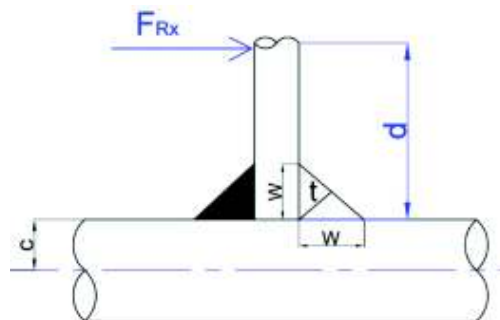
Soldadura de filete tubo-eje soporte.
